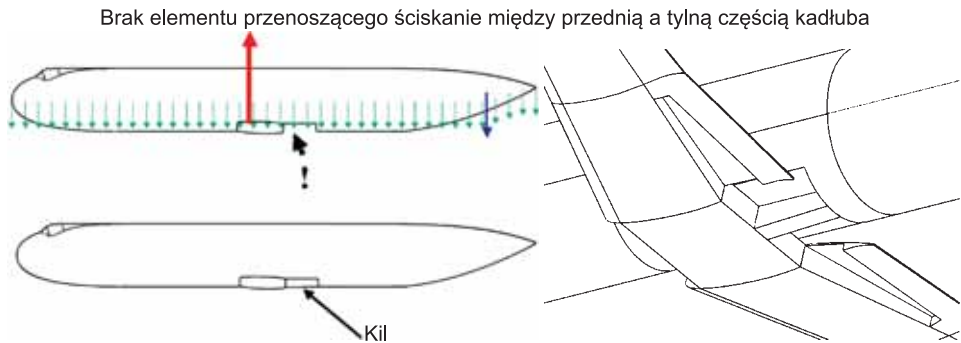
Przykłady mieszanych konstrukcji kadłuba
